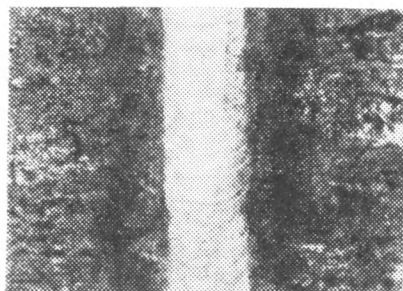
Непрерывный шов, полученный при лазерной сварке (CO₂-лазер, CrNi листовый материал, ширина шва 0,25 мм)
